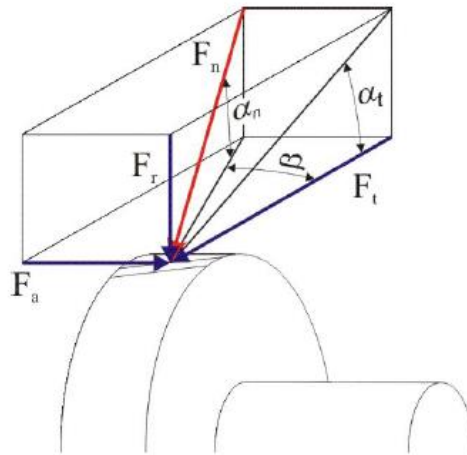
Fuerzas en un engranaje de dientes helicoidales
